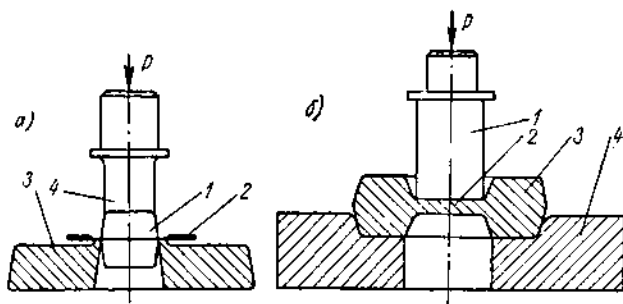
Схема обрезки облоя (а) и прошивки пленки (б)
